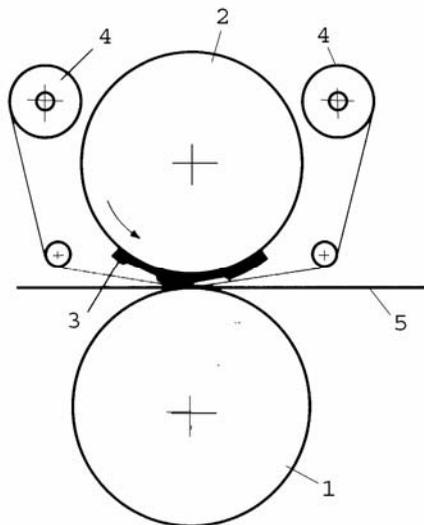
Схема ротационной секции тиснения: 1 — печатный цилиндр; 2 — формный цилиндр с электронагревательным элементом; 3 — штамп; 4 — фольговое устройство; 5 — запечатываемый материал
